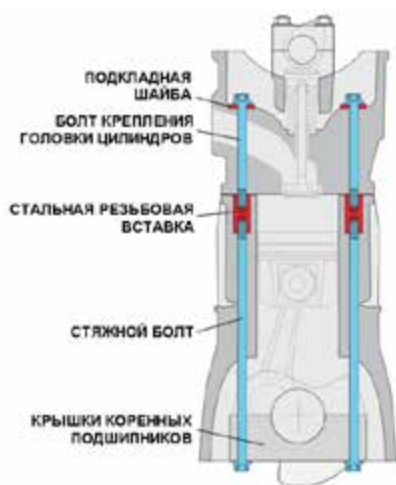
В некоторых конструкциях алюминиевых блоков цилиндров крепление крышек коренных подшипников производится длинными стяжными болтами, ввернутыми в стальные резьбовые вставки. Применение длинных стяжных болтов позволяет снизить перекос цилиндра относительно коленчатого вала, вместе с тем, снижая риск повреждения резьбового отверстия в относительно мягком металле блока цилиндров; источник: *Kolbenmidt Pierburg AG
